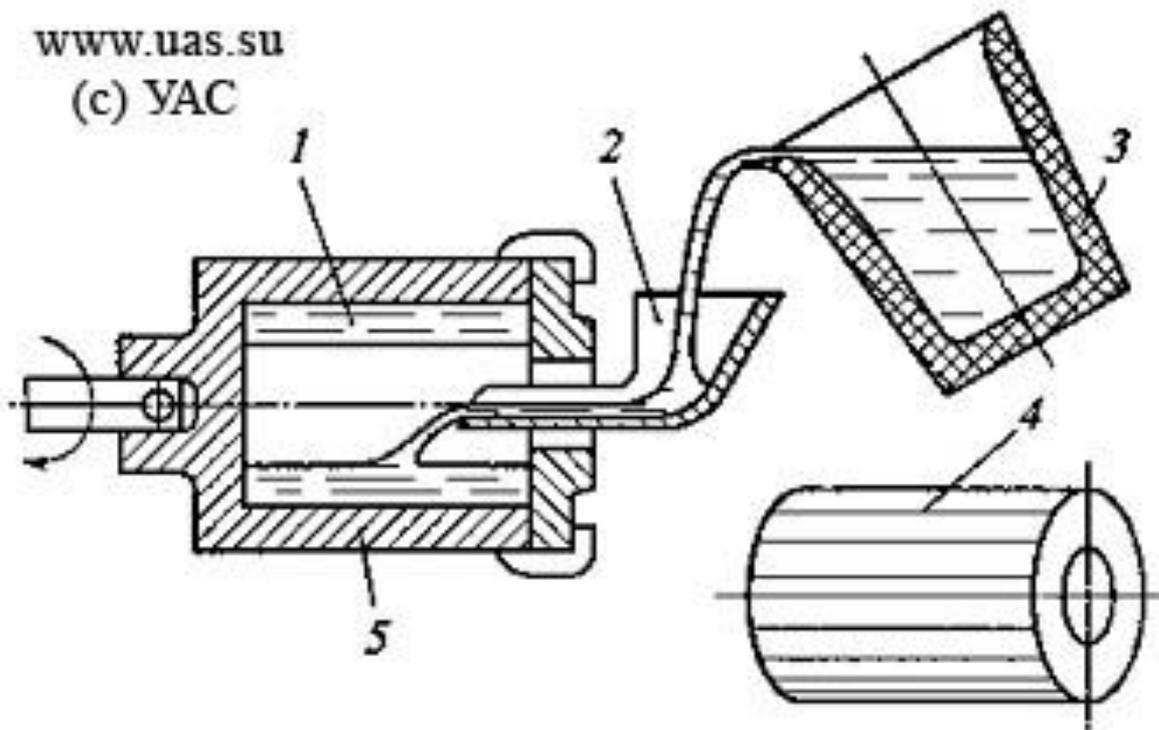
Схема получения отливки при вращении формы вокруг горизонтальной оси: 1 – расплав; 2 – заливочный желоб; 3 – ковш; 4 – отливка; 5 – форма
